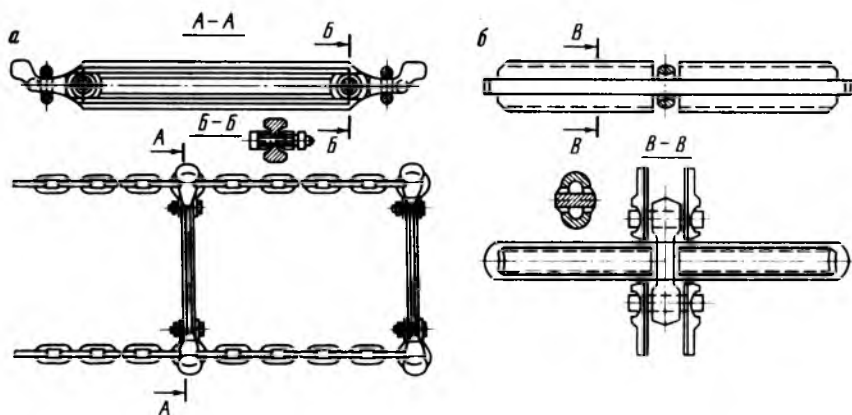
Схемы соединения скребков кольцевыми сварными (а) и разборными штампованными (б) цепями
